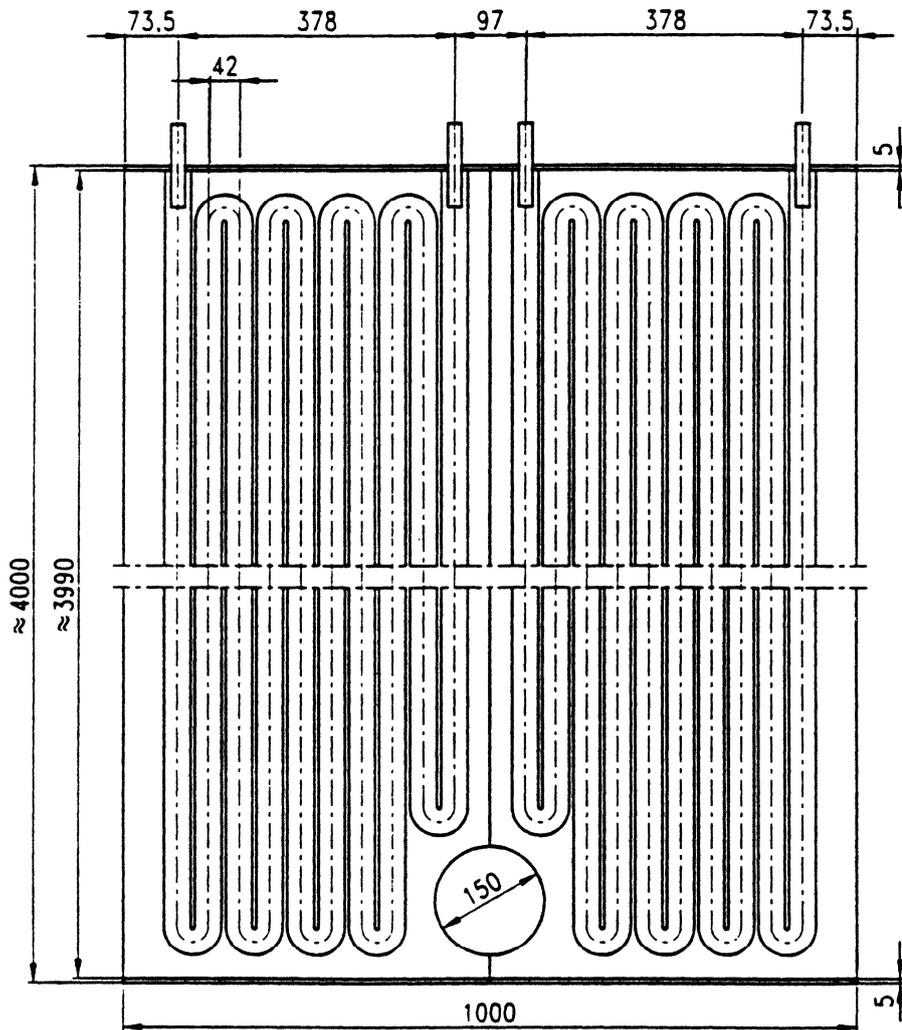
Wassergekühlte Verbundplatte mit Durchführung für äußere Anschlüsse
